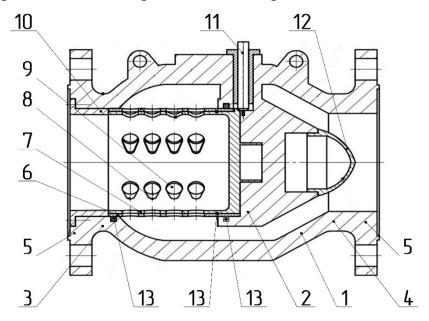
Схема осевого регулирующего клапана с запирающим устройством поворотного типа [xx]: 1 – внешний корпус, 2 – внутренний корпус, 3 – выходной патрубок, 4 – входной патрубок, 5 – фланец, 6 – делитель потока (сепаратор), 7 – запирающий орган, 8 – отверстие криволинейной формы, 9 – отверстия, 10 – расширительная втулка, 11 – вал, 12 - 3аглушка, 13 -уплотнение
